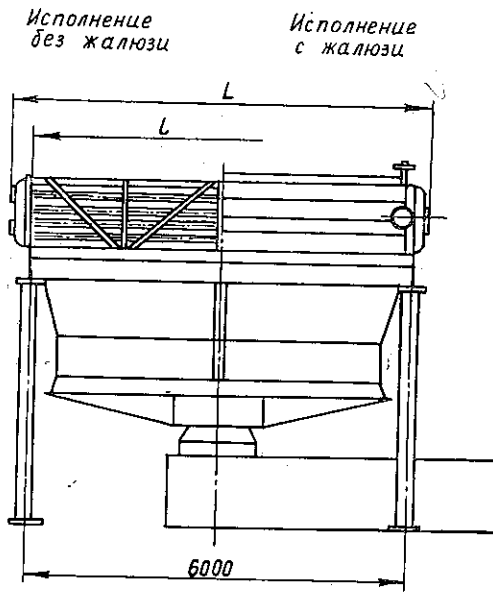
Зигзагообразный аппарат типа АВЗ с тихоходным электродвигателем и металлической опорной конструкцией
